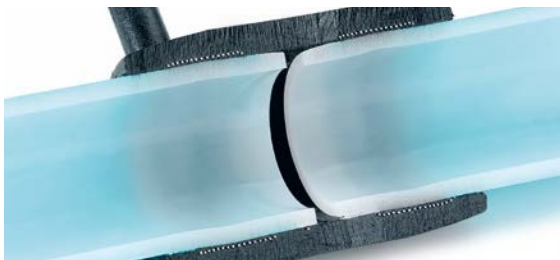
Elektroschweißmuffe im Schnitt
